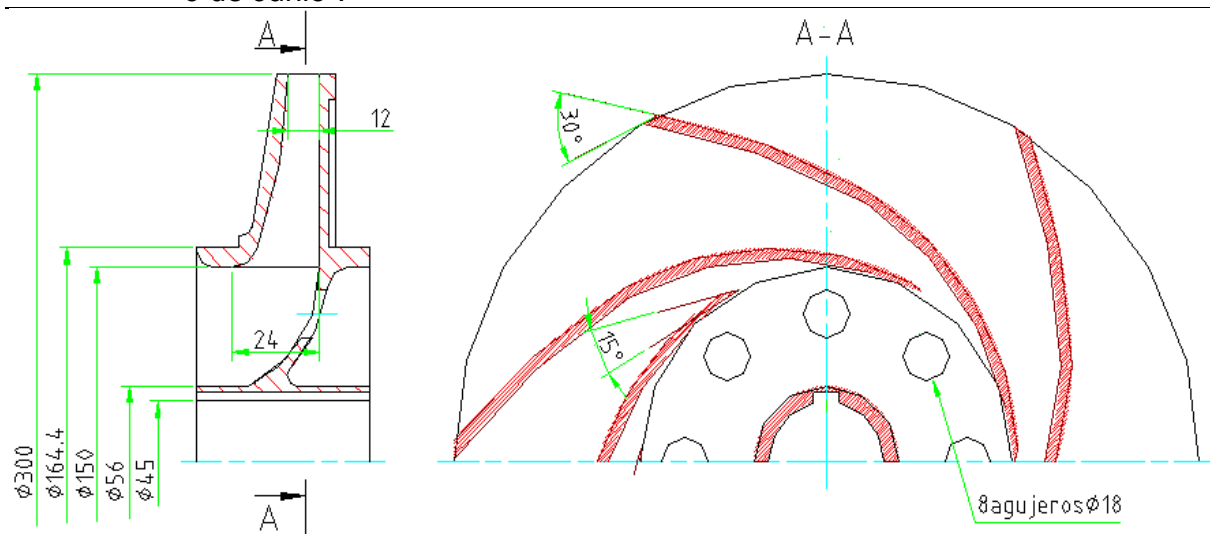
Geometría y dimensiones de uno de los impelentes de la bomba.
